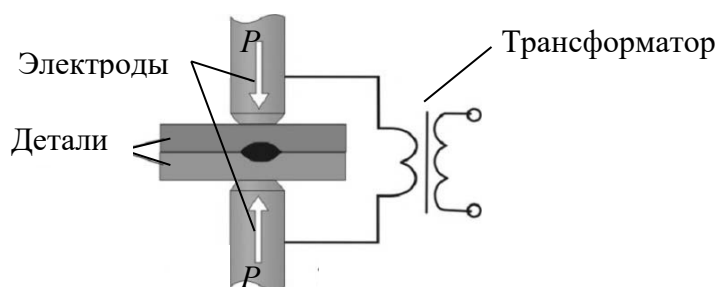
Схема точечной сварки давлением
